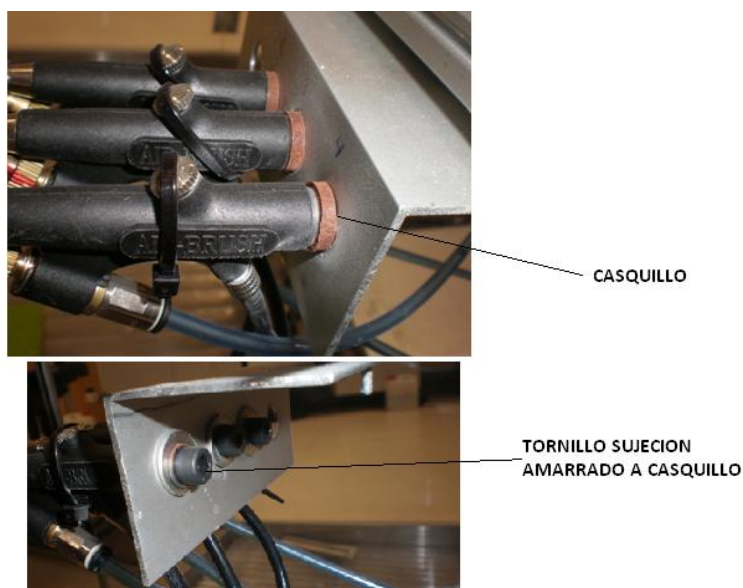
Vista montaje pistolas para PAA, PAH o lavado.
